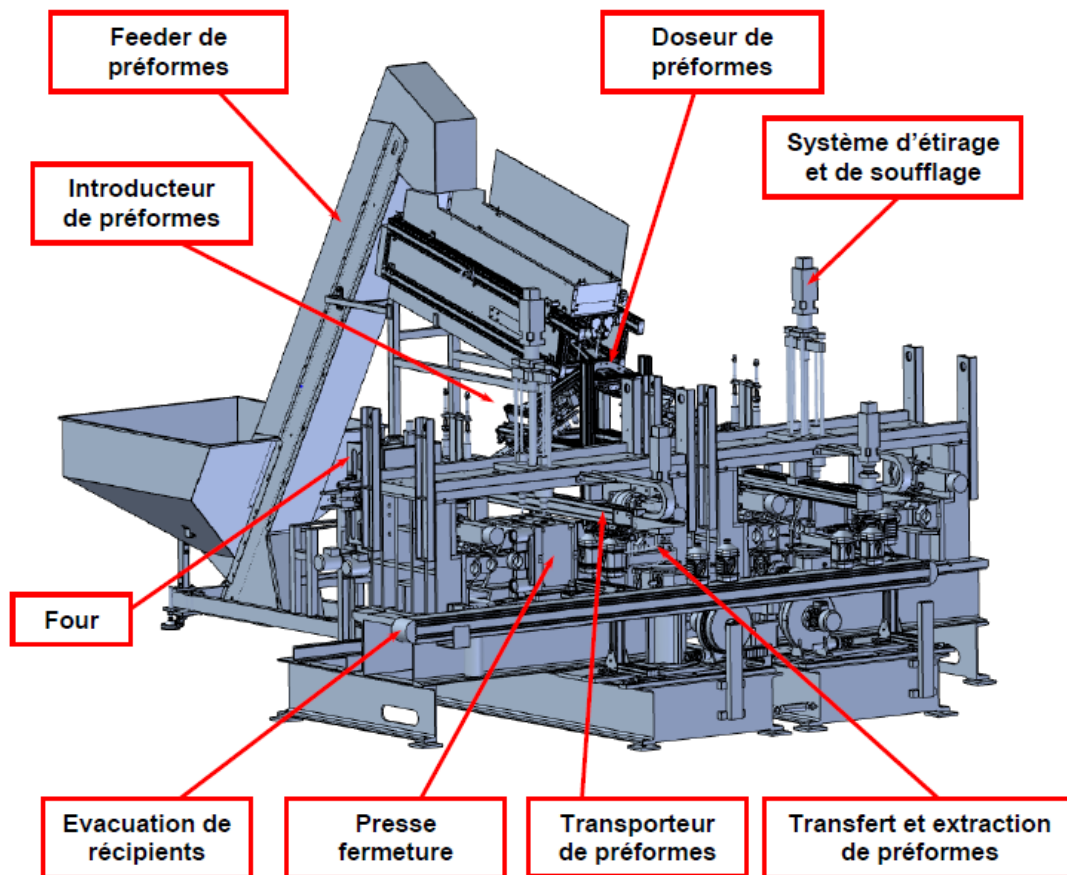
Machine d'étirage et soufflage de préformesde PET - URBI-4T [2].
